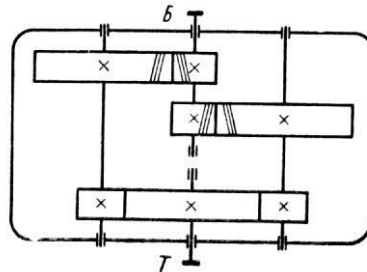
Кінематична схема двоступеневого співвісного редуктора з роздвоєною передачею
